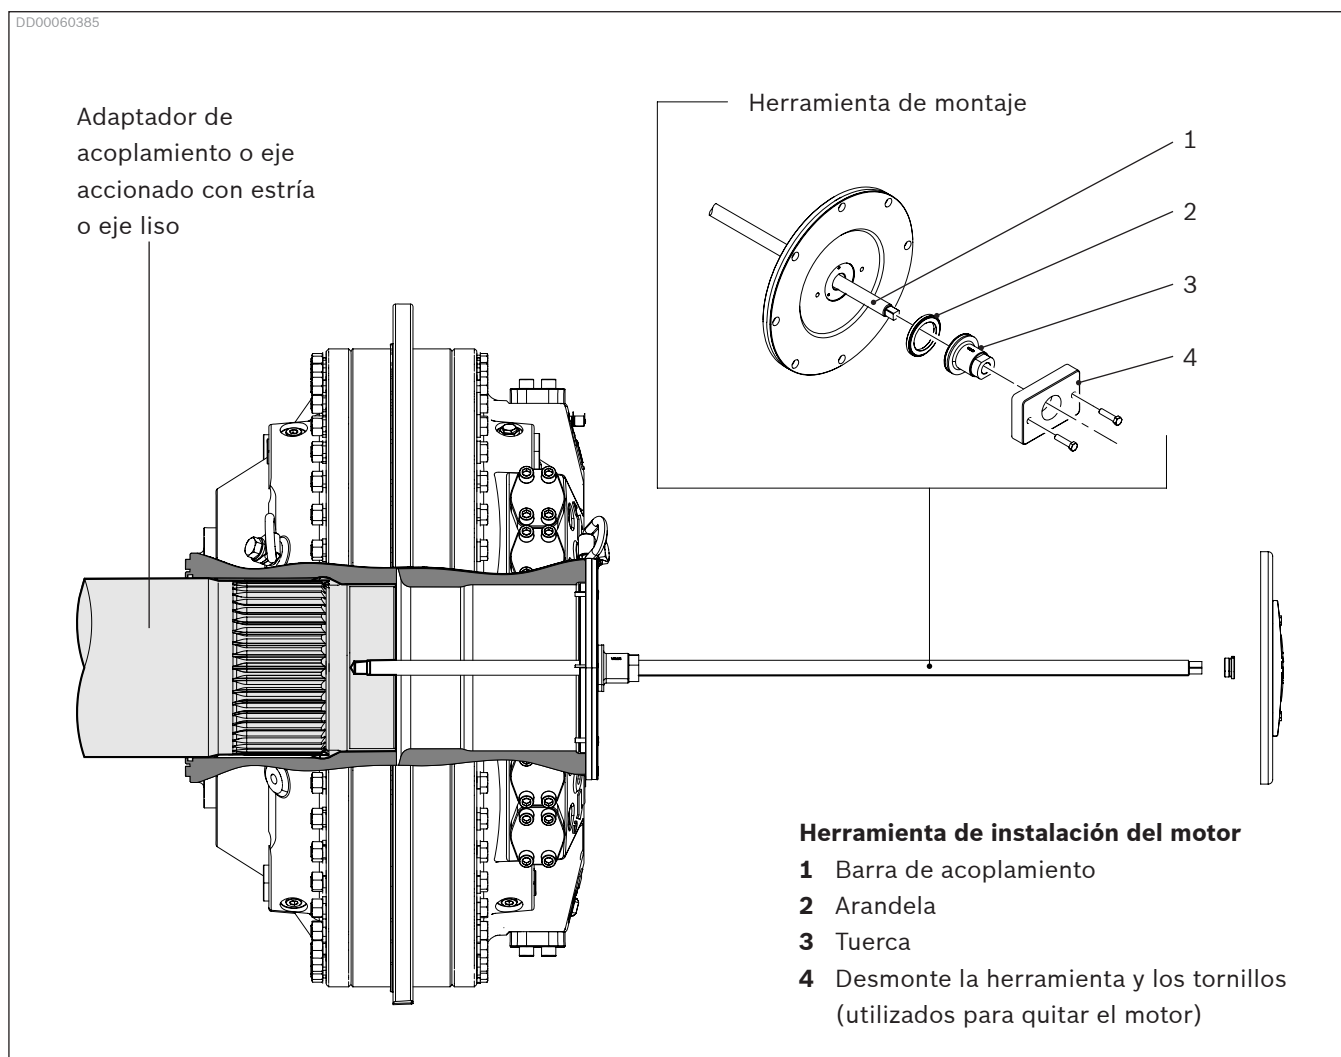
Instalación del motor CBm con la herramienta de instalación
